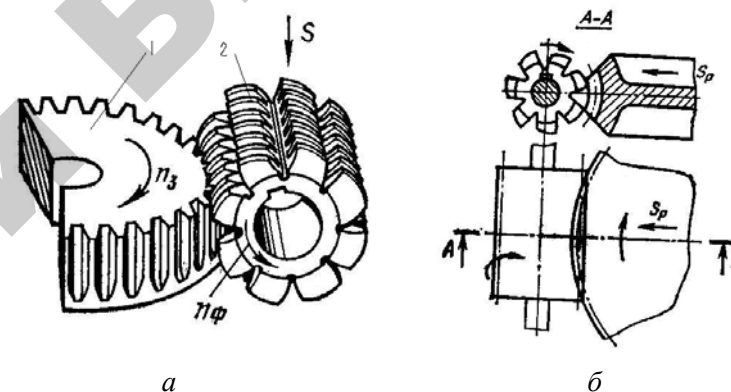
Схема нарезания зубчатых колес червячной фрезой методом обката: а – цилиндрических колес; б – червячных колес; 1 – режущий инструмент (червячная фреза), 2 – заготовка, S_b – вертикальная подача; n_3 – частота вращения заготовки, V_ϕ – скорость вращения фрезы
